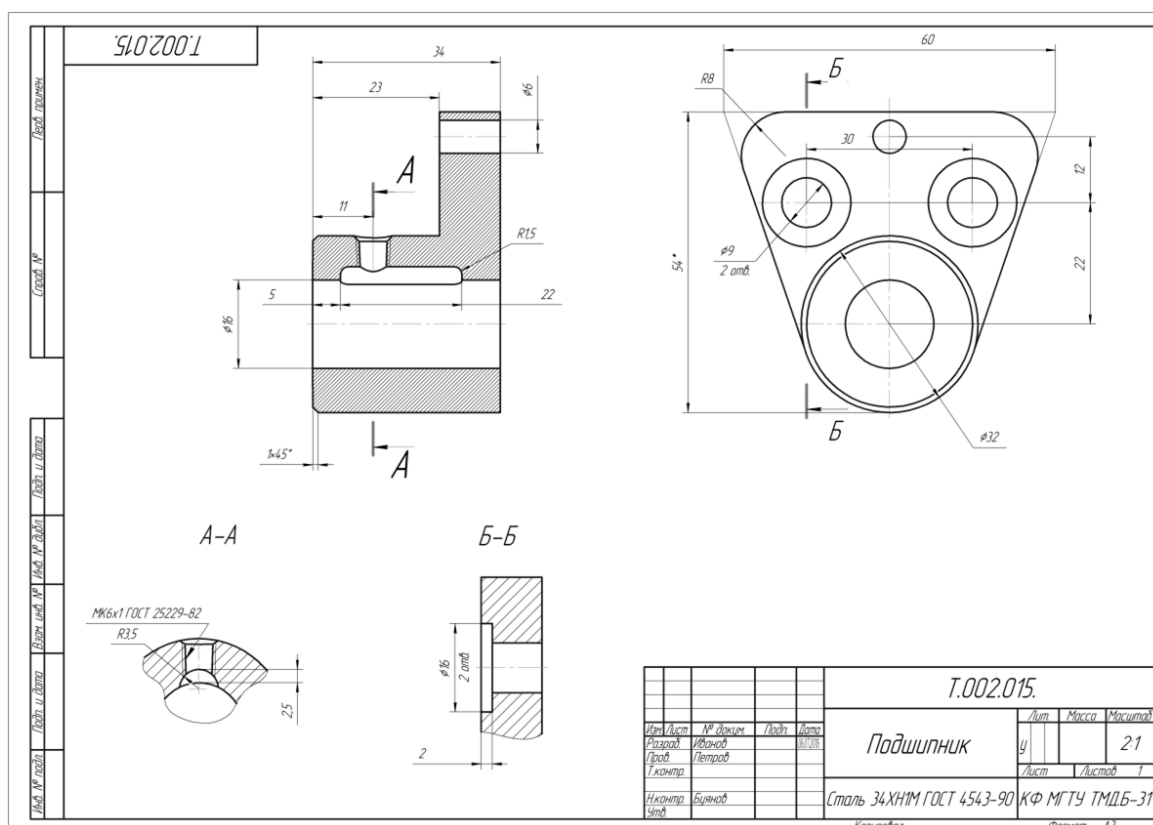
Учебный чертеж детали для создания трехмерной твердотельной модели
